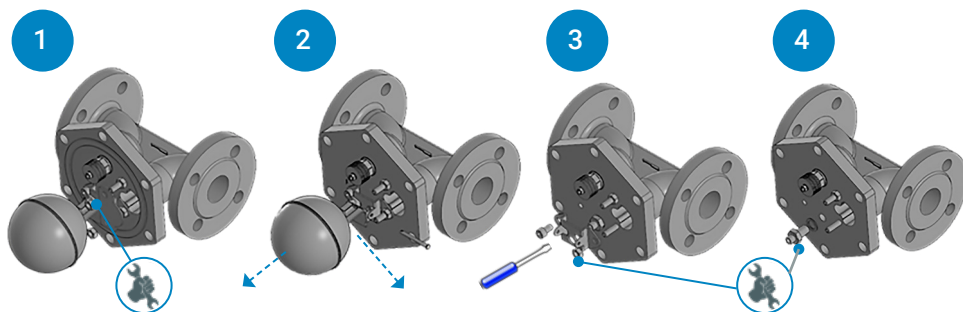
Демонтаж поплавка и поплавкового механизма.
